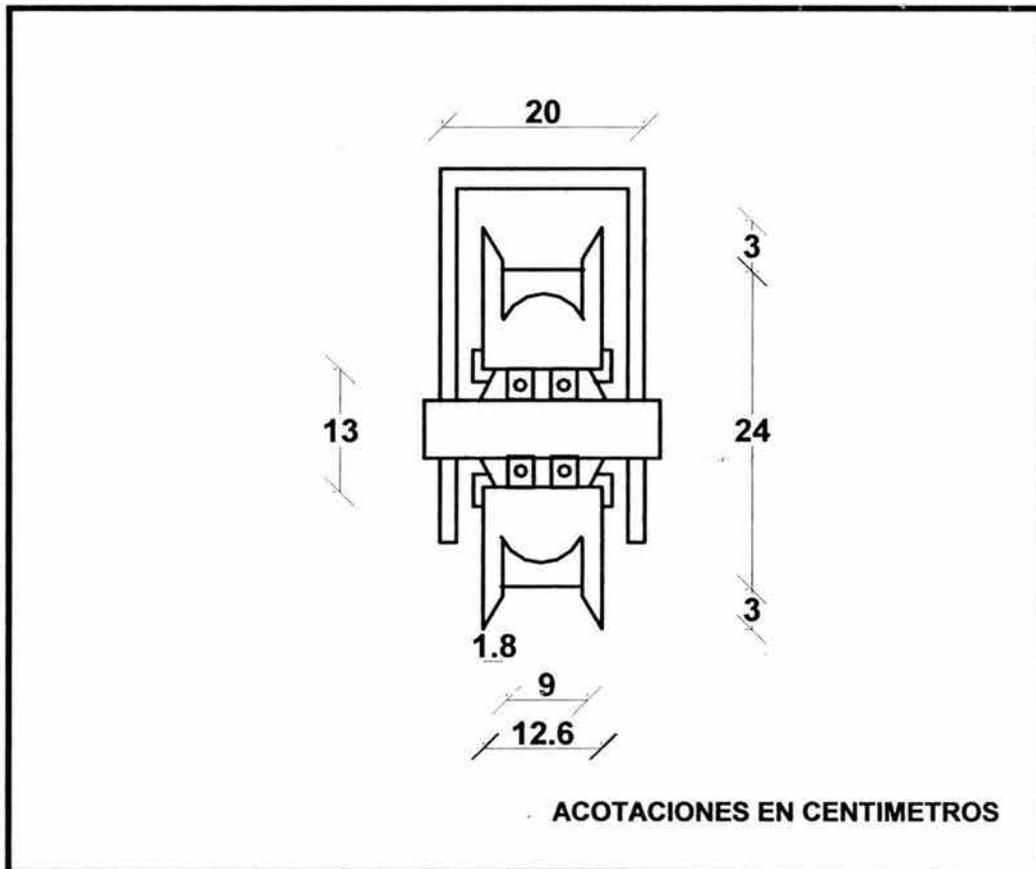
DETALLE DE LA RUEDA DEL CARRO DE MONTAJE
